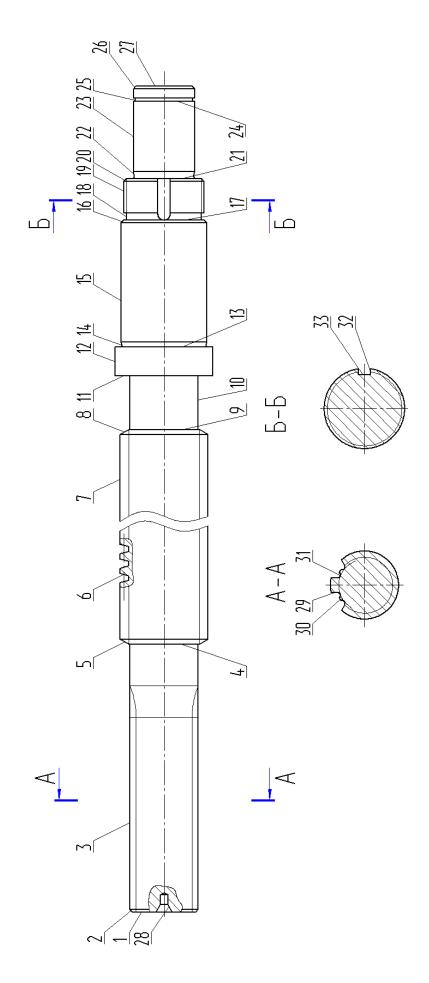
Систематизация поверхностей детали «Винт» 7
